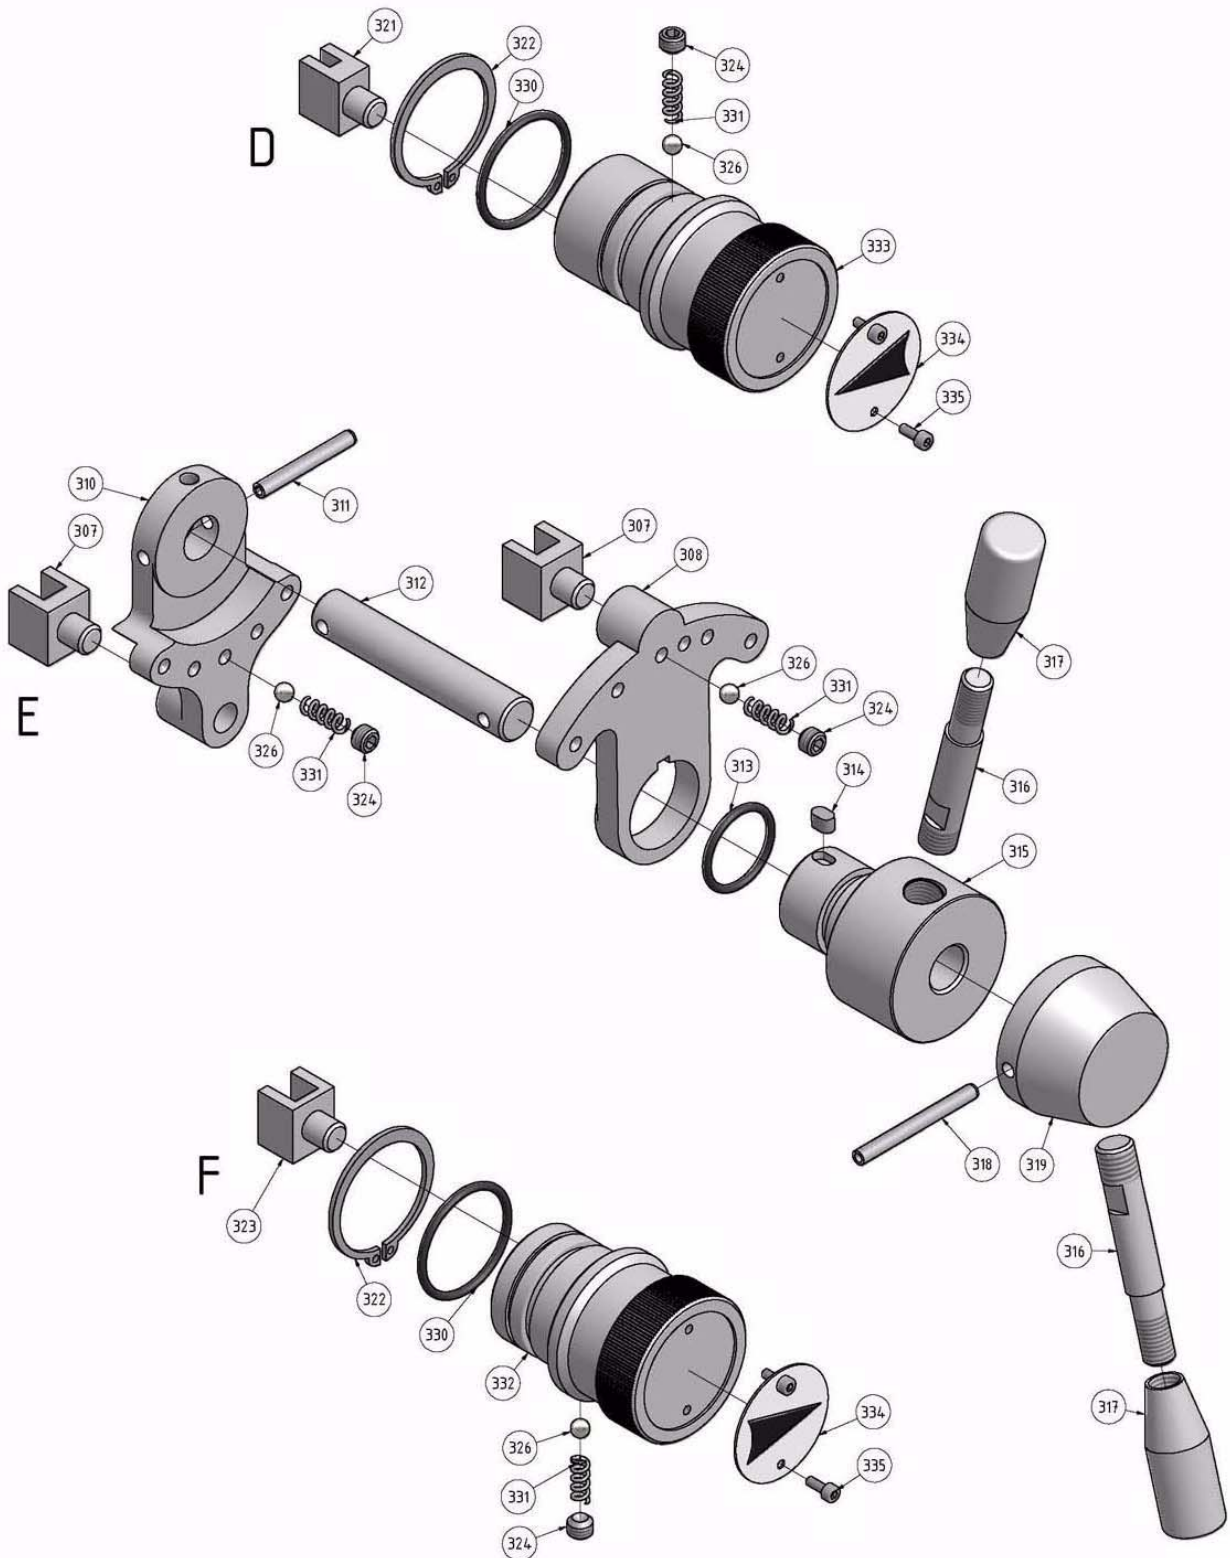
Vorschubgetriebe 4-4 - Feed gear 4-4
